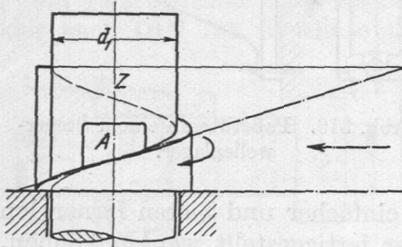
Verwandtschaft zwischen Schraube und Keil.
